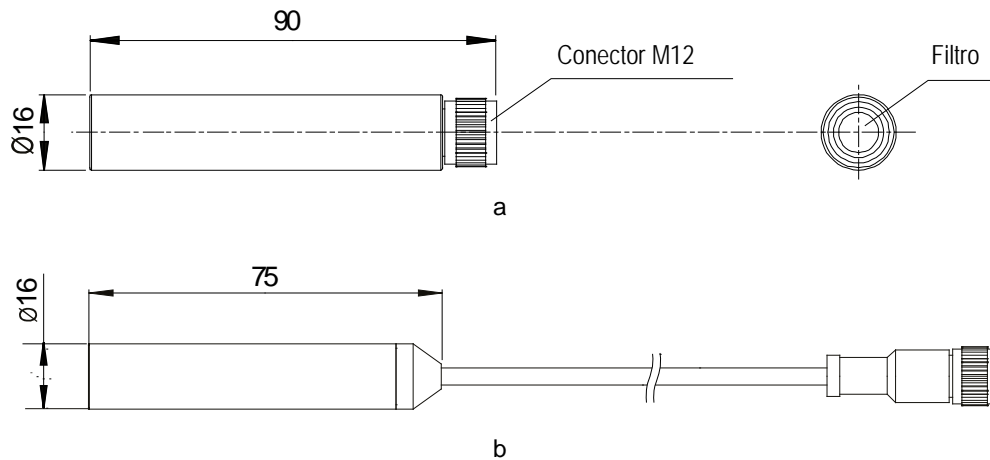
Sondas remotas: a – SP16; b – HD16
